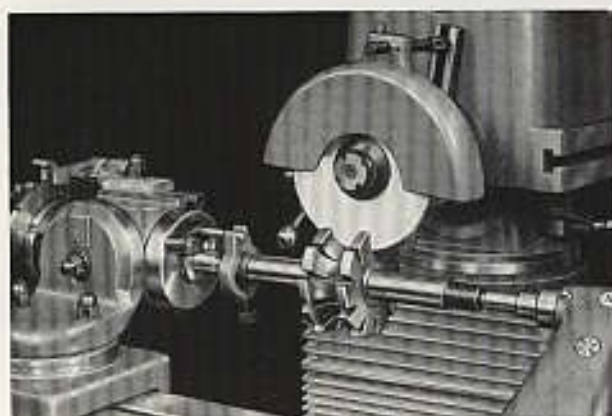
, Schleifen der Spanfläche an einem zwischen Spitzen gespannten Formfräser
